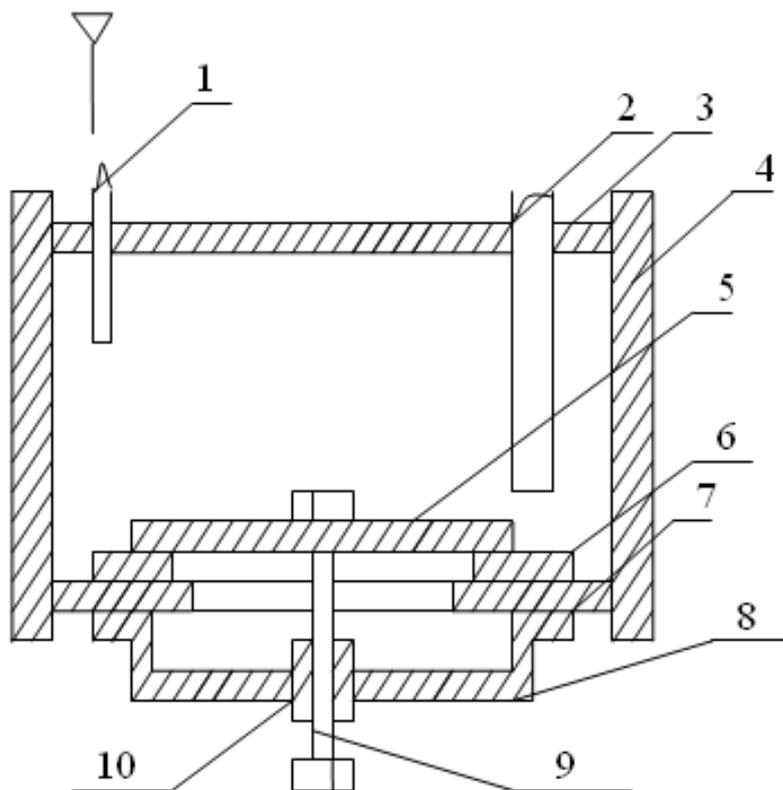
Насос замещения: 1 - воздушная труба; 2 - водоподъемная труба; 3 - верхняя крышка; 4 - корпус; 5 - клапан; 6 - уплотнительное кольцо; 7 - днище; 8 - направляющая; 9 - шток клапана; 10 - втулка
